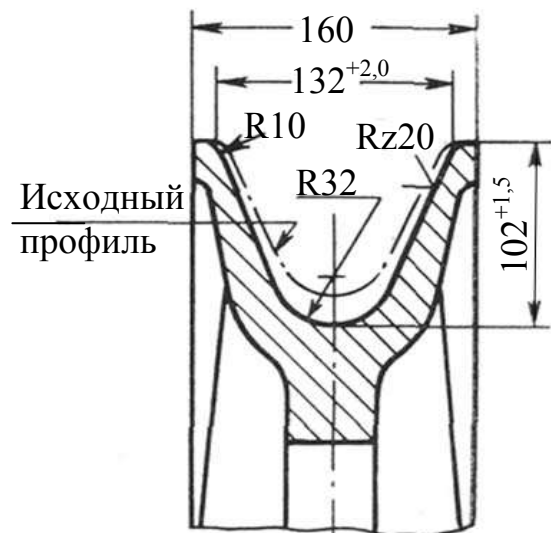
Ремонтный чертеж восстановления проточкой ручья блока наводки
